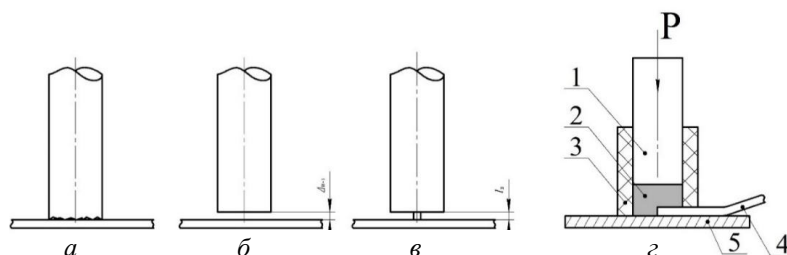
Различные схемы сопряжения соединяемых разнородных деталей при импульсной сварке с магнитным воздействием
